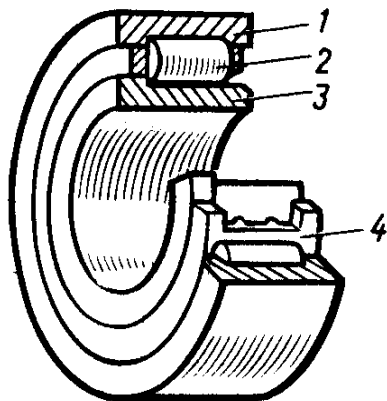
Задній циліндричний роликовий підшипник
